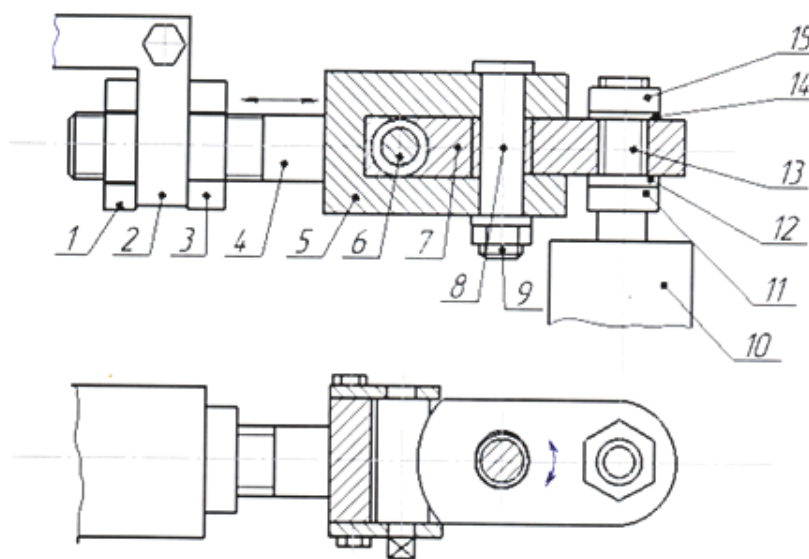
Конструктивная схема устройства регулирования положения огнеупорного моноблока относительно выпускного канала промежуточного ковша МНЛЗ
